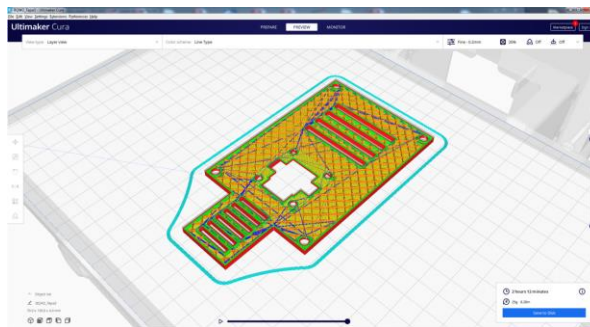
Vista de la tapa que muestra el proceso de impresión.
